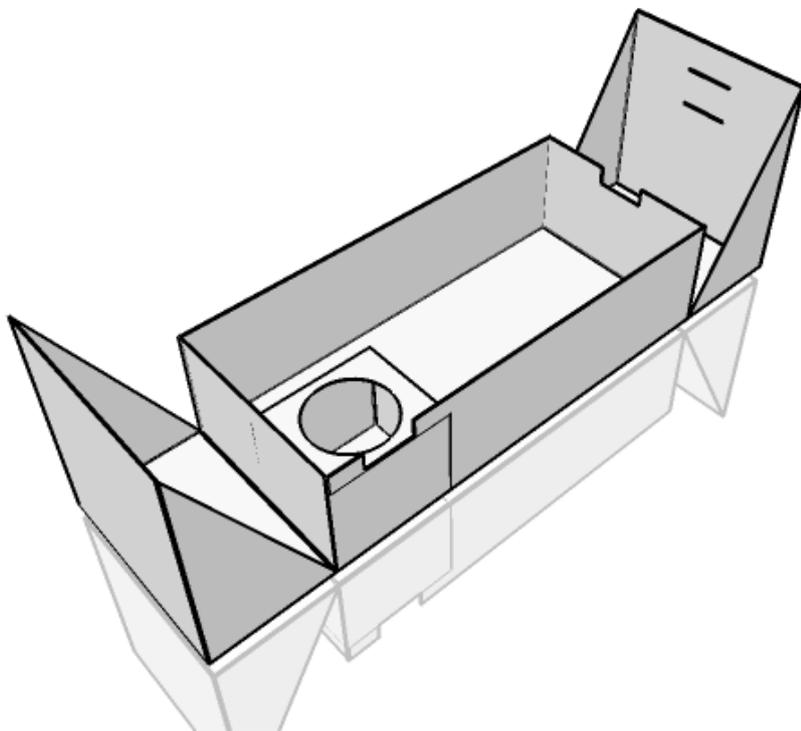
Guía de plegado. Plegado caja finalizado. Fuente: Elaboración propia.
